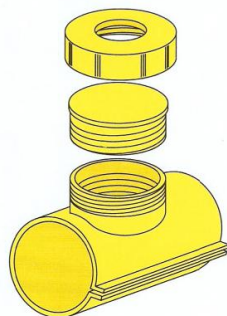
Accesorio Electrosoldable de Balonamiento
